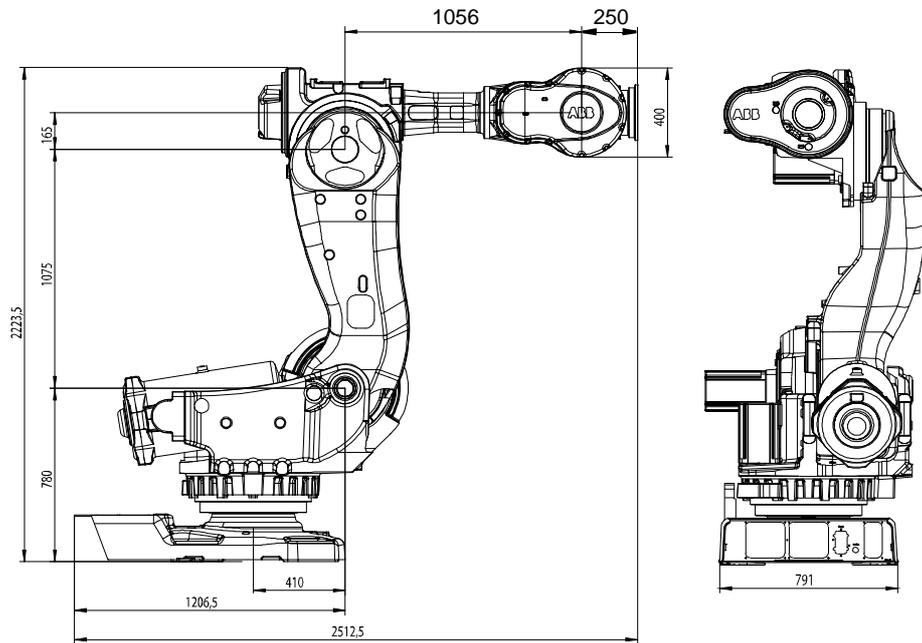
Vues latérale et arrière du manipulateur (dimensions en mm). Derrière le pied du manipulateur, laissez 200 mm pour les câbles.
